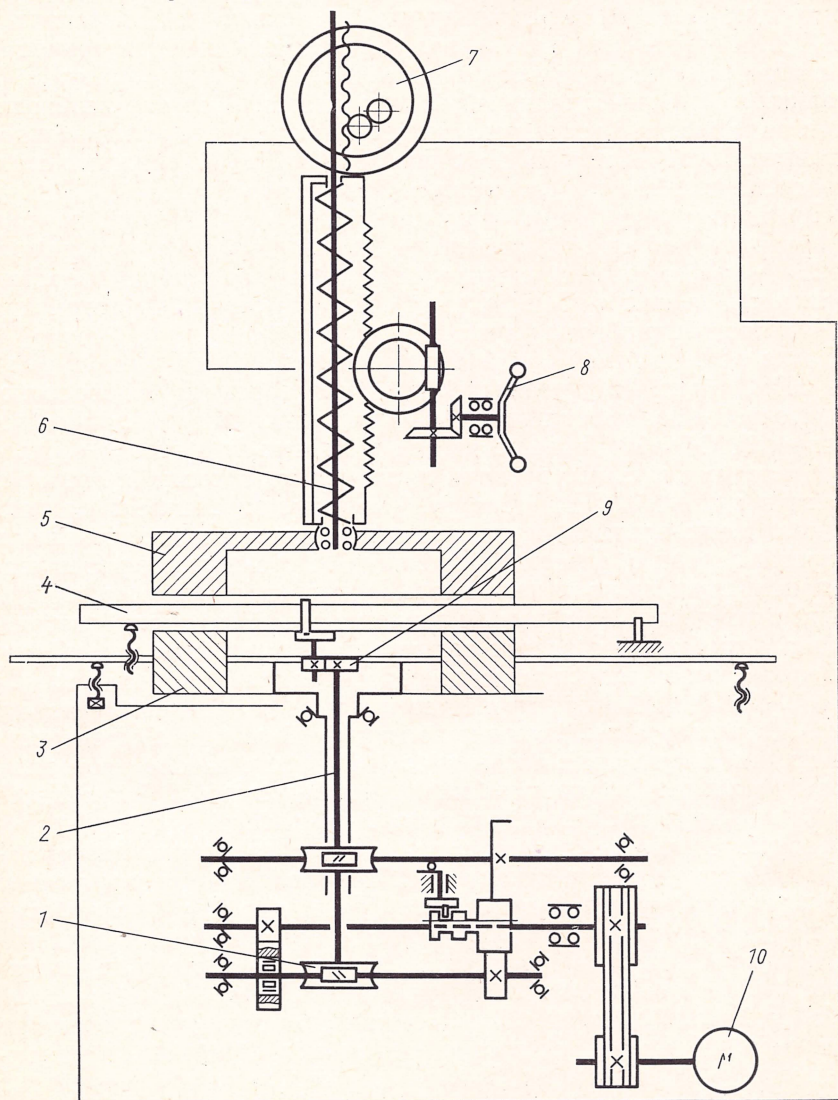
Кинематическая схема универсального вертикально-доводочного станка 3Б814
